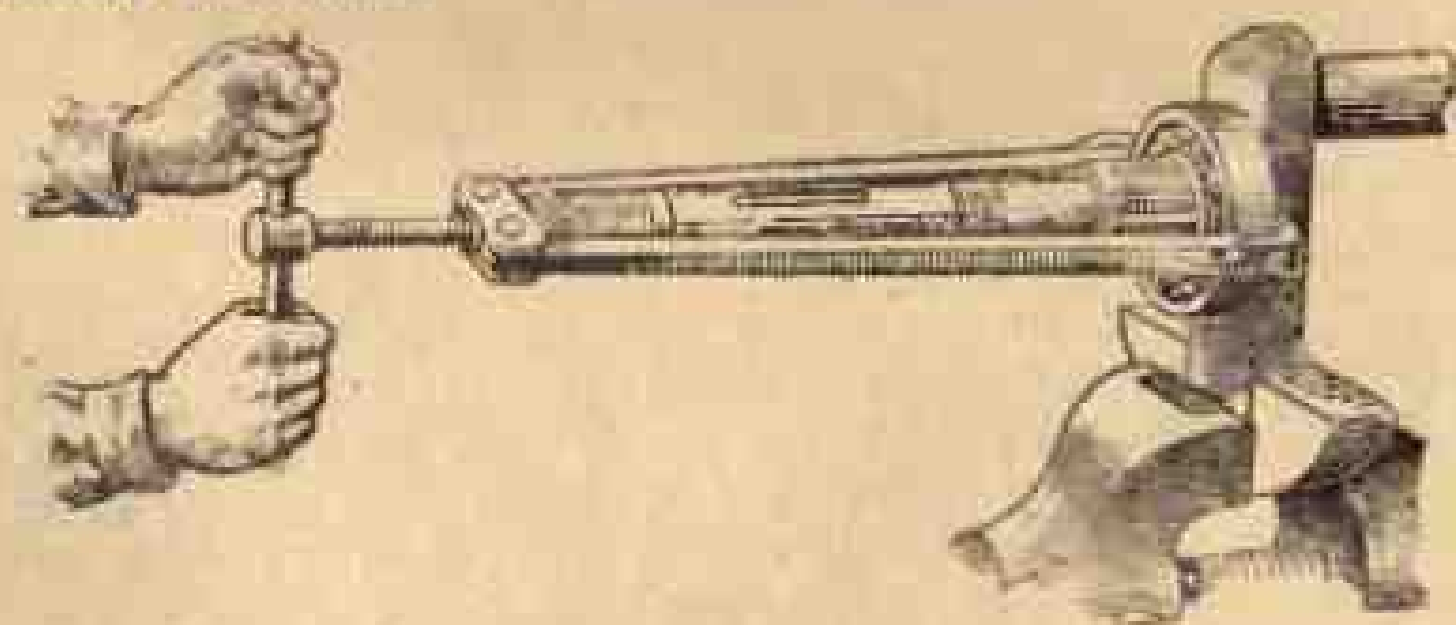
Снятие переднего опорного подшипника захватом конического вала и тисках
